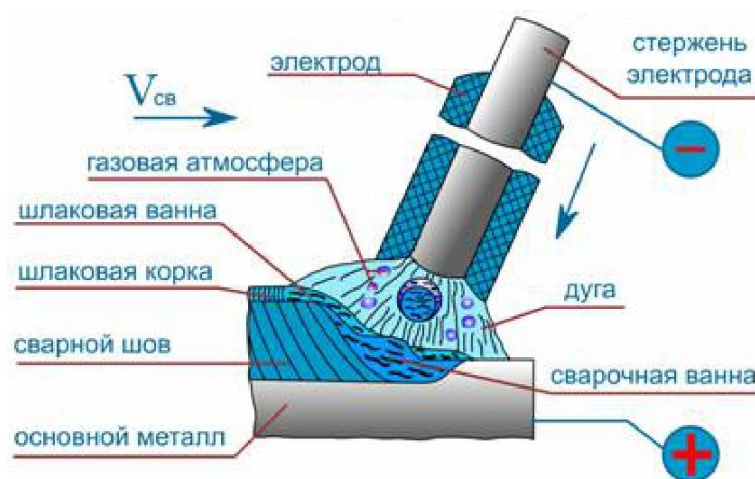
Схема выполнения ручной дуговой наплавки
